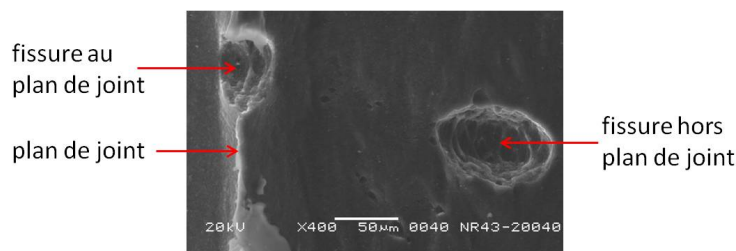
Localisation, au plan de joint et hors plan de joint.
